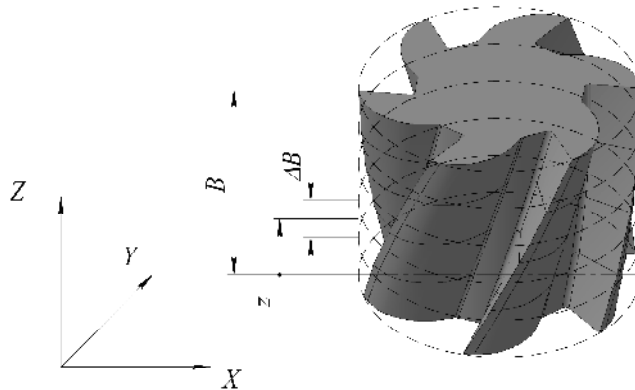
Разбиение рабочей части фрезы на элементарные слои
